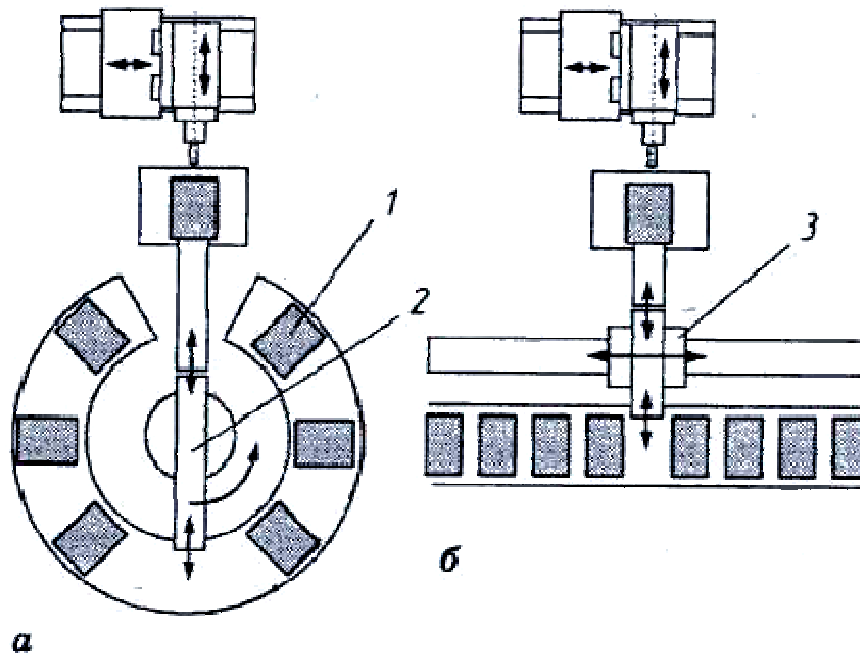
Неподвижные магазины палет, используемые в ГПМ для обработки корпусов:
